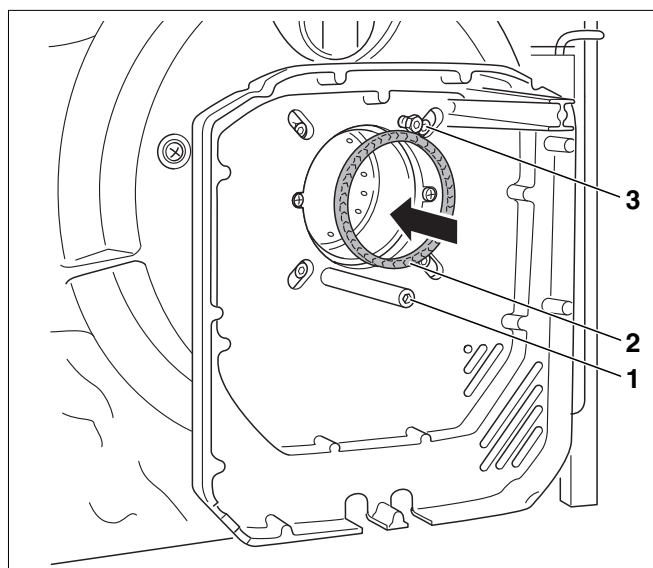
Colocación de la junta en los modelos de quemador 17 hasta 45
